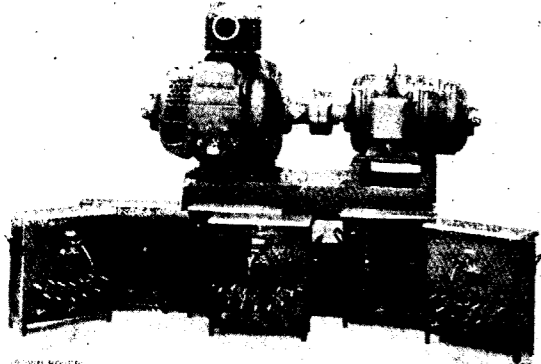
º.—Grupo de soldadura por arco para la alimentación de tres electrodos de 180 amperios cada uno con tres grupos de reguladores de la corriente de soldadura.
